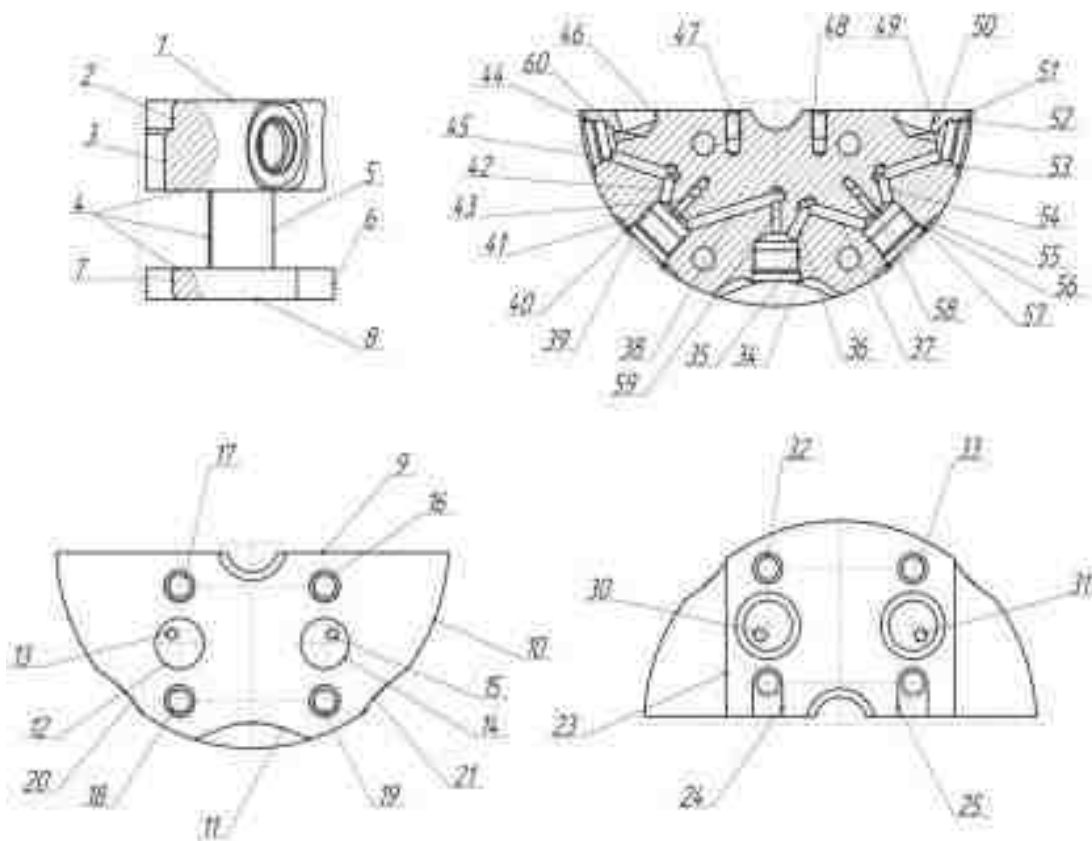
Эскиз детали «Корпус блока клапанного»
